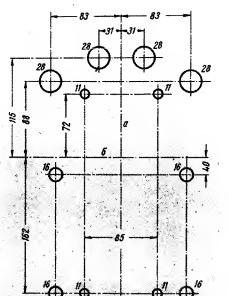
Сверление отверстий для установки на изоляционных пластинах контакторов типа КТП 524 и КТП 544 с задним присоединением
